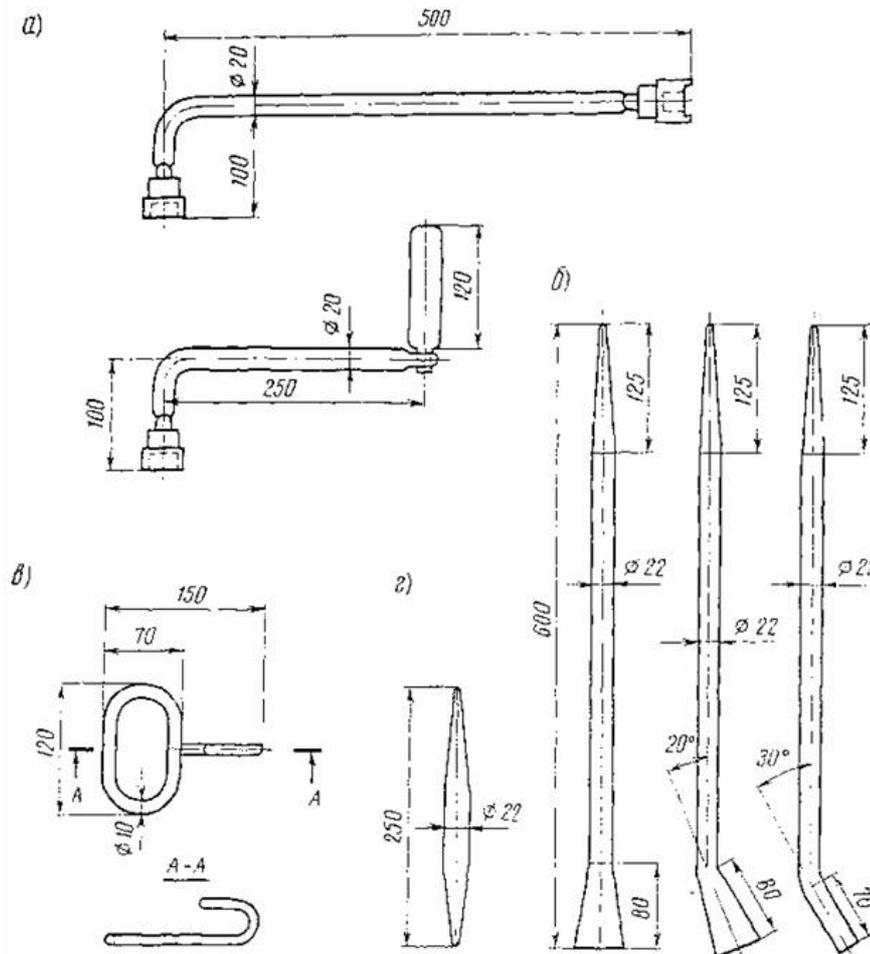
Вспомогательные инструменты для сборки СМГК
